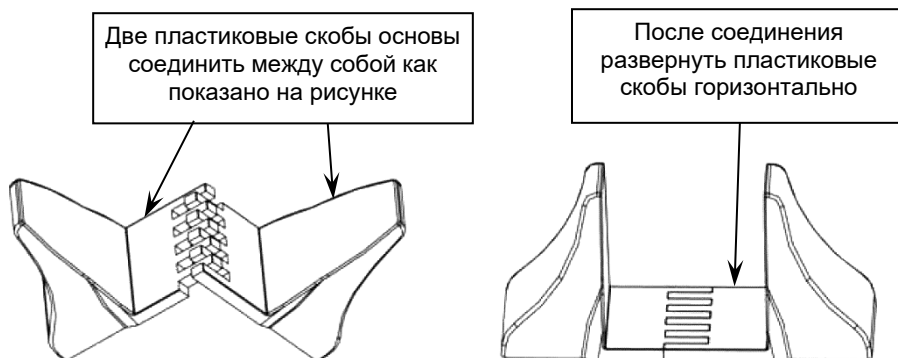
Сборка пластиковых основ для вертикальной установки изделия.
